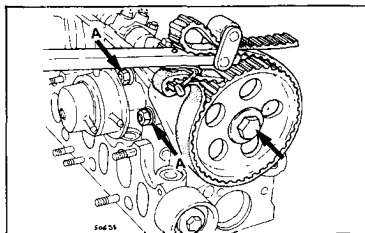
Используйте специальный инструмент Renault для снятия зубчатого шкива распревала
